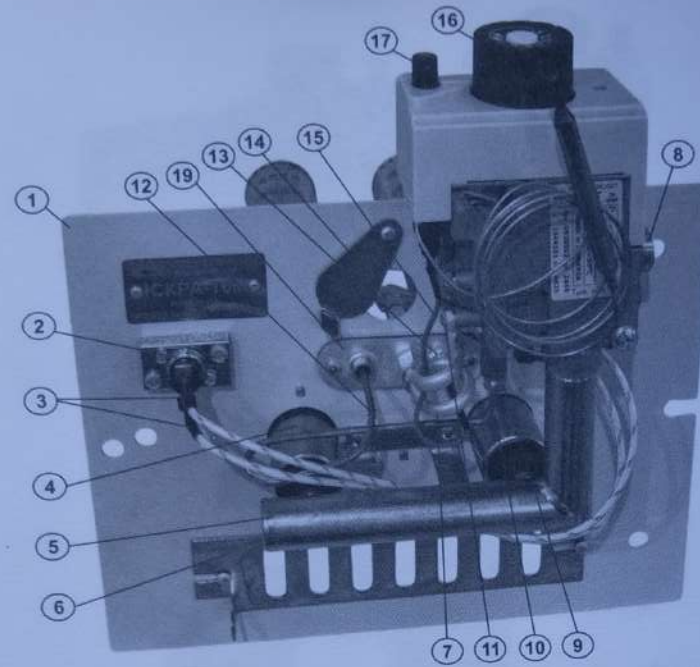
Пристрій газопальниковий ІСКРА модернізована (вид спереду)
